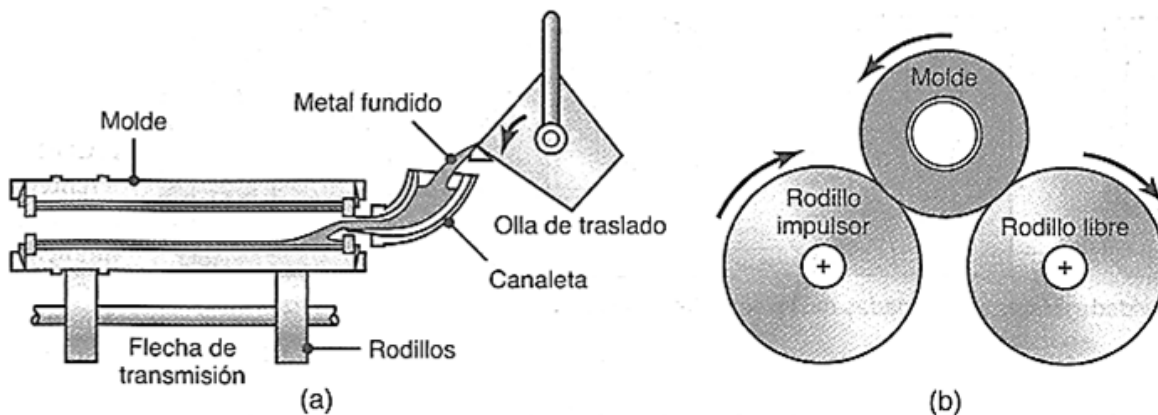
Esquema del proceso de fundición centrífuga: a) Vaciado del metal en el molde; y b) Giro del molde impulsado por el rodillo impulsor [2].
